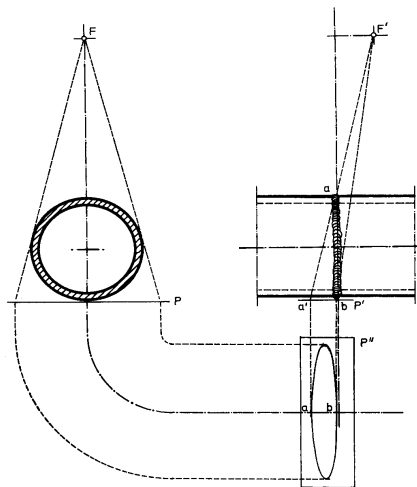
Técnicas "en perspectiva" o "en elipse" para la radiografía de soldaduras circulares en tuberías de pequeño diámetro.
